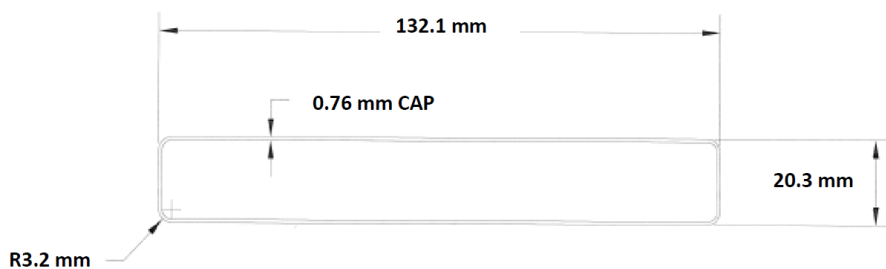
Profil plein des planches « SLS » et « Ultra Light »
